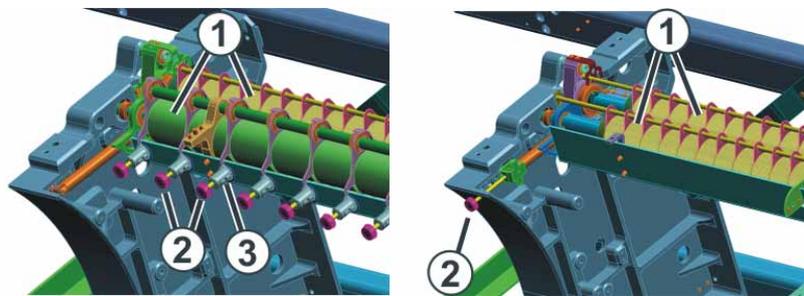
Hauptabzug (rechtes Bild: CMS 420 E)
